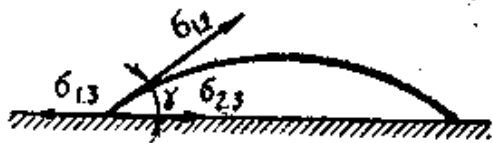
Умова рівноваги краплі розплавленого припою на металевій поверхні
